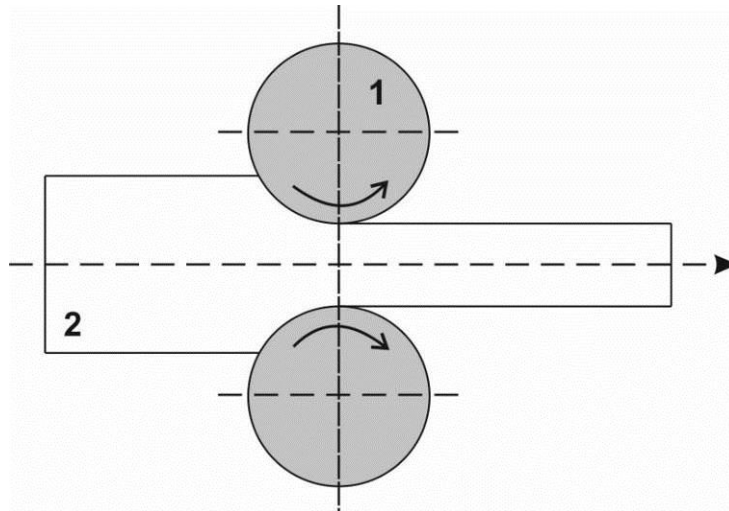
Схема листовой прокатки: 1 - валки, 2 – обрабатываемый лист
